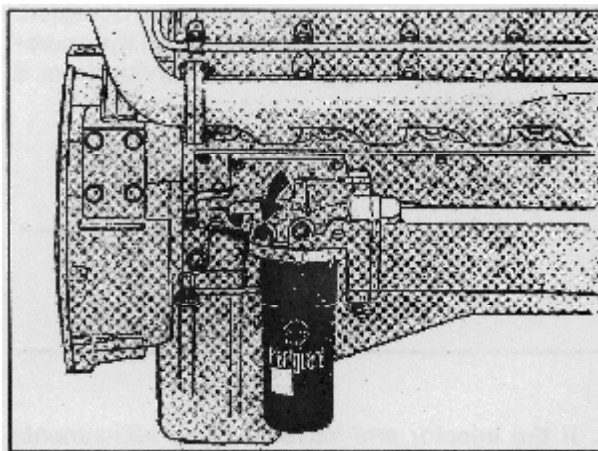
(OM 1002 L) Точка заправки системы смазки. Двигатель VT-903.
